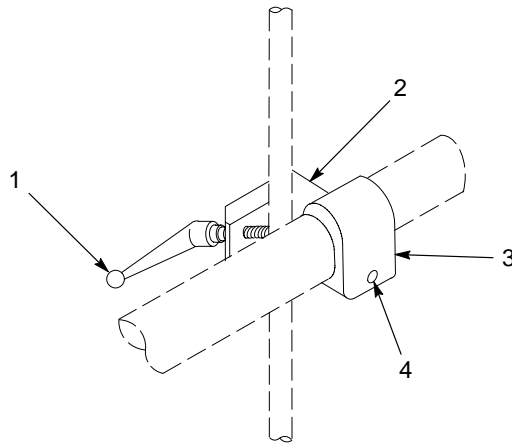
Conjunto standard de barra de pistola, para pistolas com tubo de suporte
